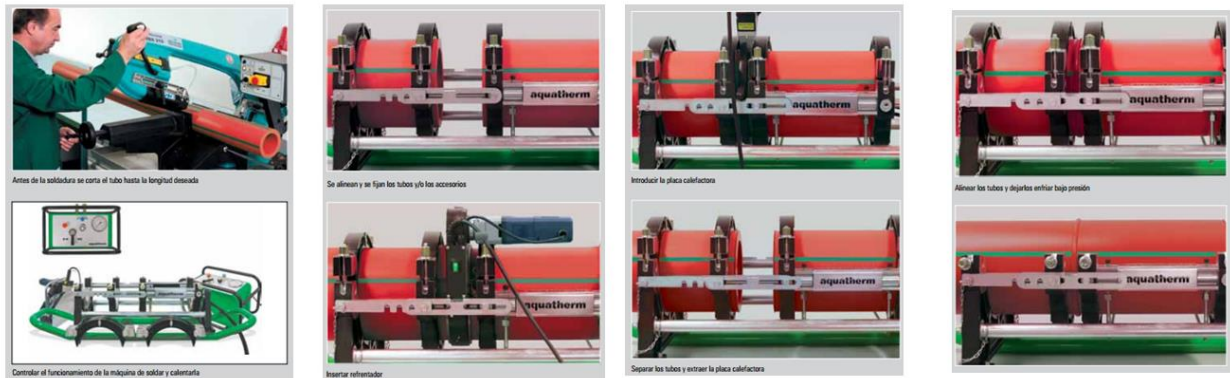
Soldadura con termofusión: soldadura a tope. Parámetros
